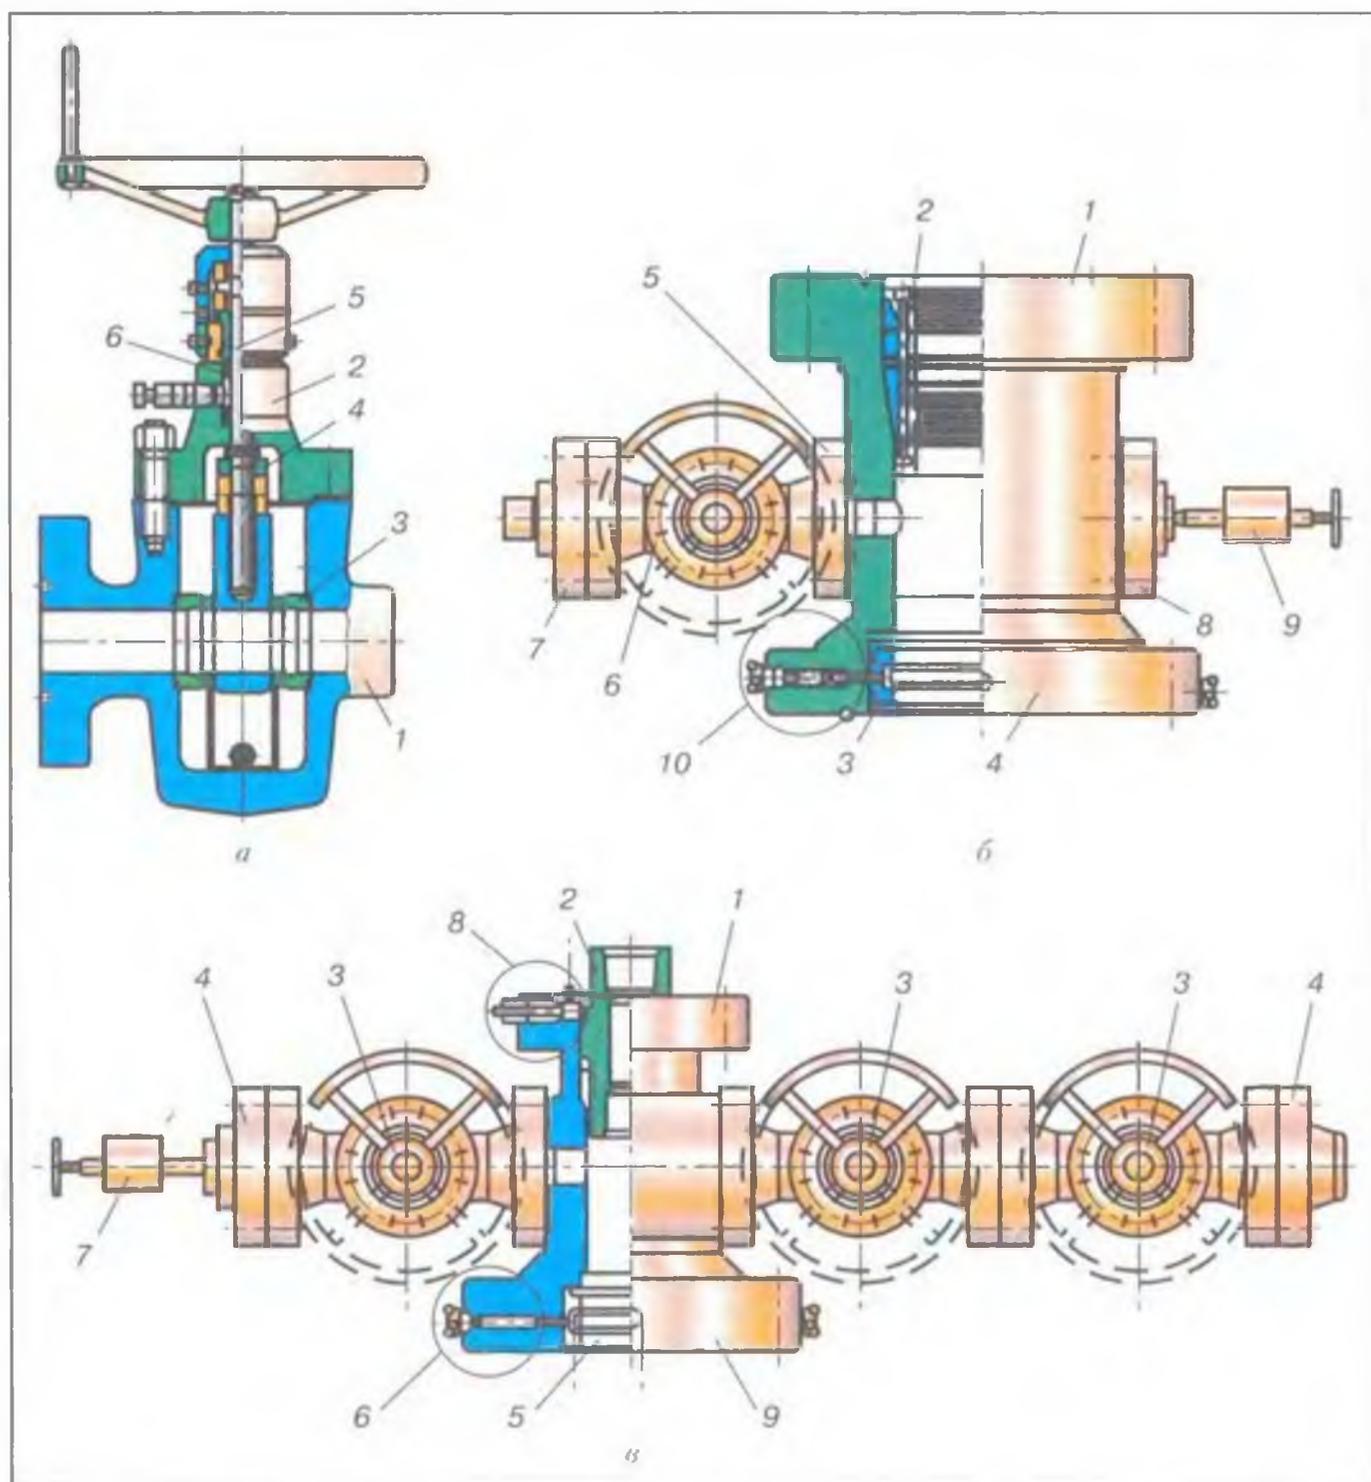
Устьевое оборудование: а – задвижка (1 – корпус; 2 – крышка; 3 – седло; 4 – шибер; 5 – шток; 6 – сальниковое уплотнение); б – колонная головка с оснасткой (1 – корпус головки; 2 – клинья обсадной трубы; 3 – вторичное уплотнение; 4, 5, 8 – соответственно нижний, боковой и резьбовой фланцы; 6 – задвижка; 7 – буфер; 9 – игольчатый вентиль; 10 – устройство для нагнетания смазки); в – трубная головка с оснасткой (1 – корпус трубной головки; 2 – адаптер для насосно-компрессорных труб; 3 – задвижка; 4 – фланцы; 5 – вторичное уплотнение; 6 – устройство смазки; 7 – игольчатый вентиль; 8 – стопорные болты с уплотнением; 9 – фланец).
